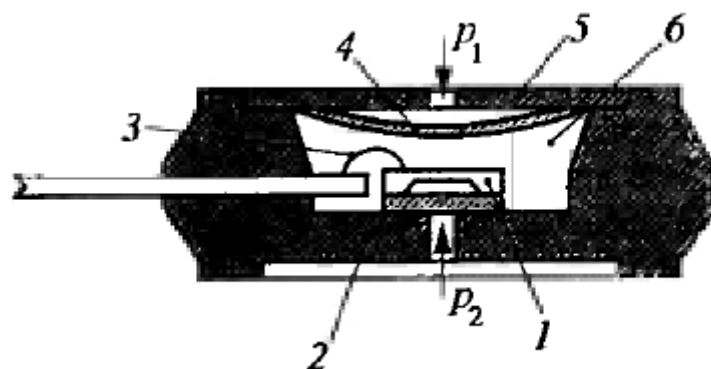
Конструктивна схема кремнієвого датчика тиску: 1- ЧЕ (мембрана); 2- корпус; 3- з'єднувальний провід; 4-кремнієва пластина; 5-сталева пластина; 6- гель
